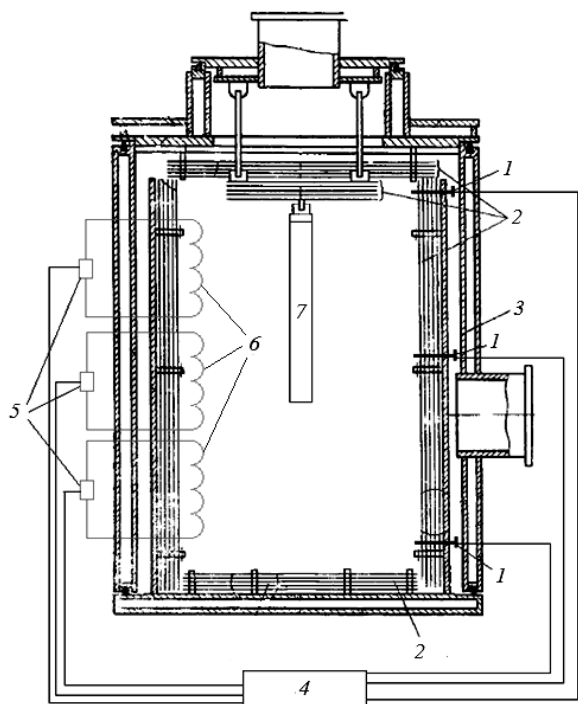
Типичная схема устройства вакуумного печного агрегата: 1 – датчики температуры; 2 – экраны из молибдена; 3 – цилиндр из нержавеющей стали (вспомогательный кожух); 4 – контроллер; 5 – преобразователи напряжения; 6 – нагреватели; 7 – отжигаемое изделие
